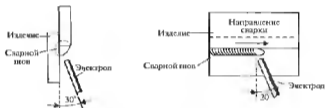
Положение электрода при сварке нахлесточного соединения однопроходным угловым швом в потолочном положении
